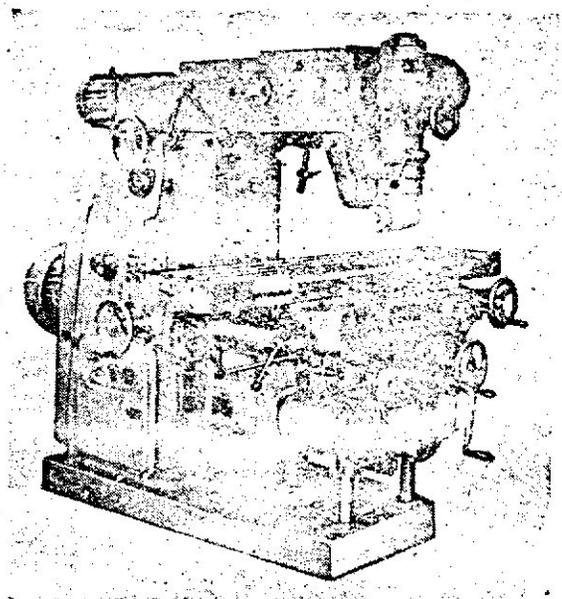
а. Широкоуниверсальный консольно-фрезерный станок модели 6М83Ш
